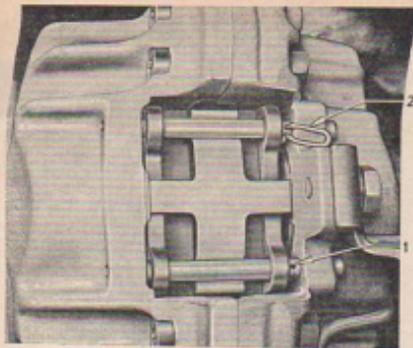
Lager der Bohrung für Sicherungsöse in Haltestift für Bremsbeläge
